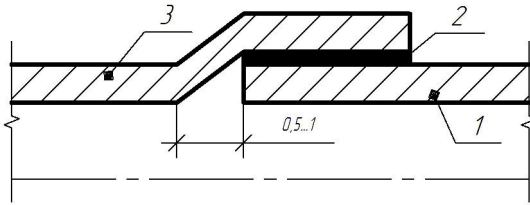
Контактне стикове зварювання поліетиленових труб: 1-з'єднувальний гладкий кінець труби, 2- зварний шов, 3-з'єднувальний кінець труби з розтрубом.
